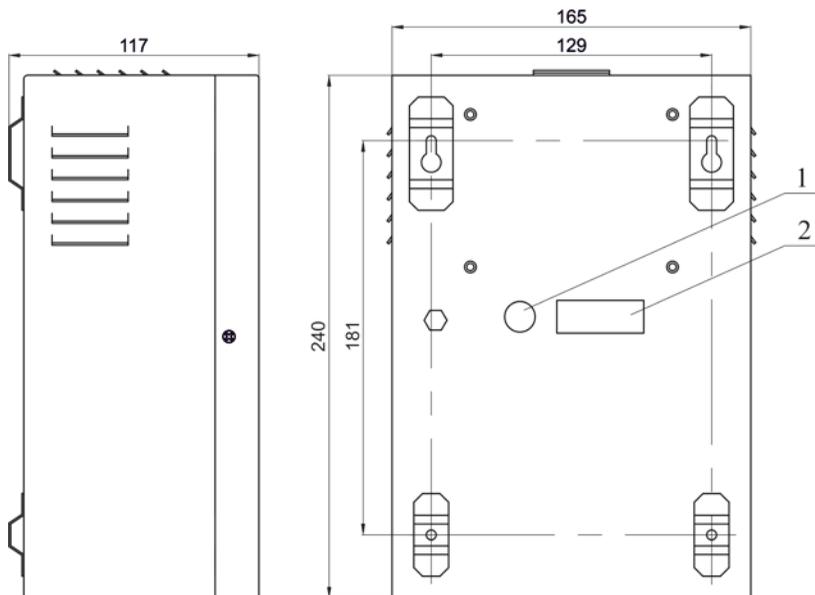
Габаритные и установочные размеры прибора ВЭРС-РИП12.
